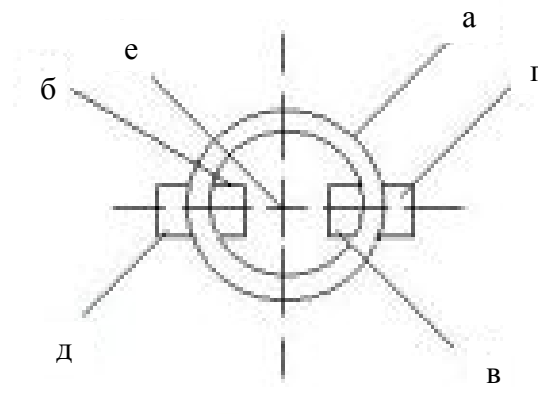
Торический разметчик – вид сверху: а – цилиндрическое кольцо; б, в – первые два выступа; г, д – вторые два выступа; е – центр симметрии
